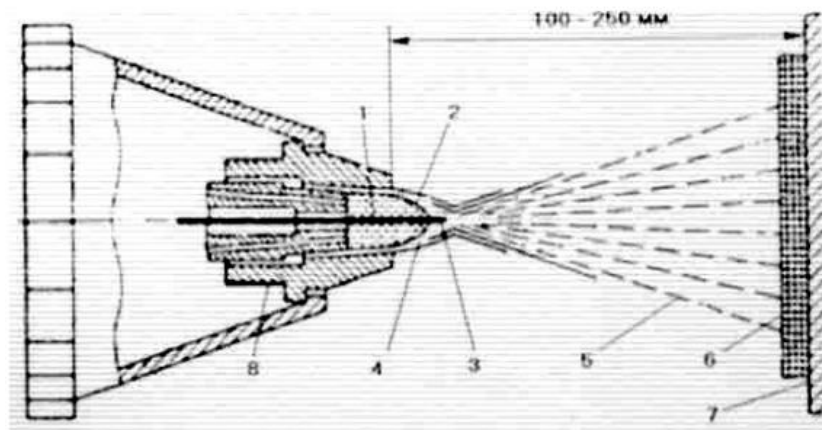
Газополуменеве наплення дротом: 1 – дріт (пруток або гнучкий шнур); 2 – полум’я; 3 – кінець дроту, що оплавляється; 4 – повітряний струмінь; 5 – частинки напилюваного матеріалу; 6 – покриття; 7 – основа; 8 – насадка
